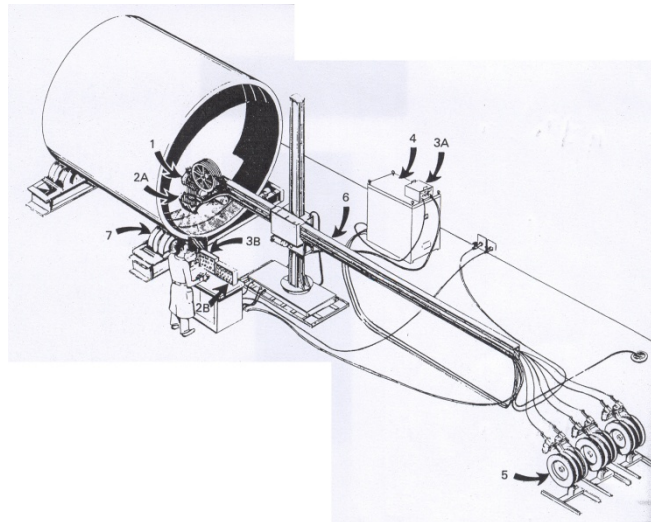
Zavarivanje konstrukcije od dupleks čelika debljine 30-40 mm. [4]
